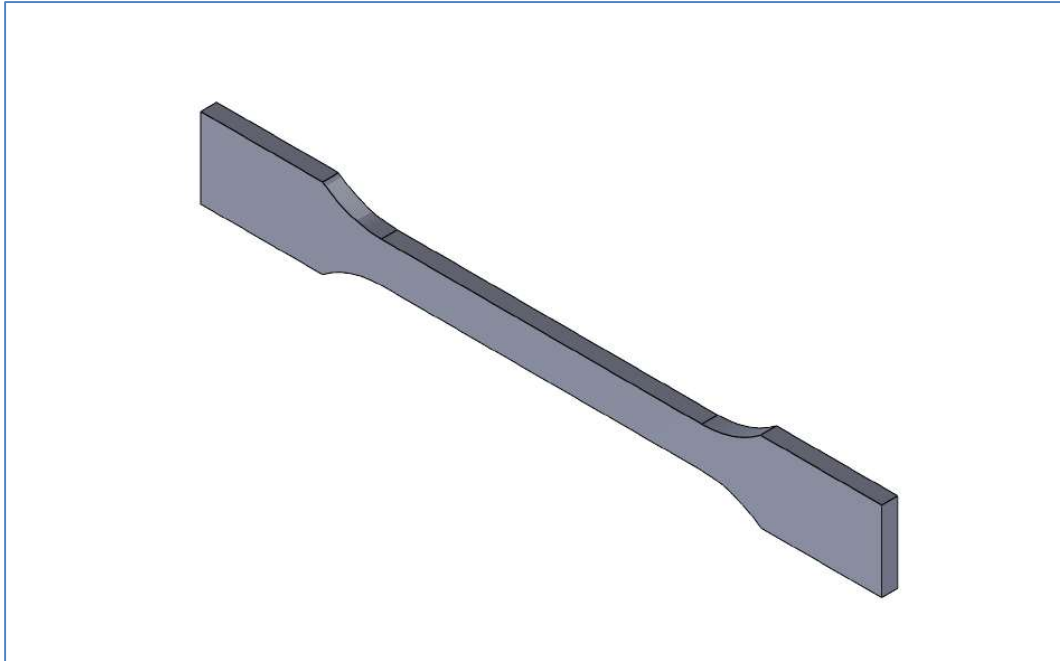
Vistas de la probeta para el ensayo de tracción.
